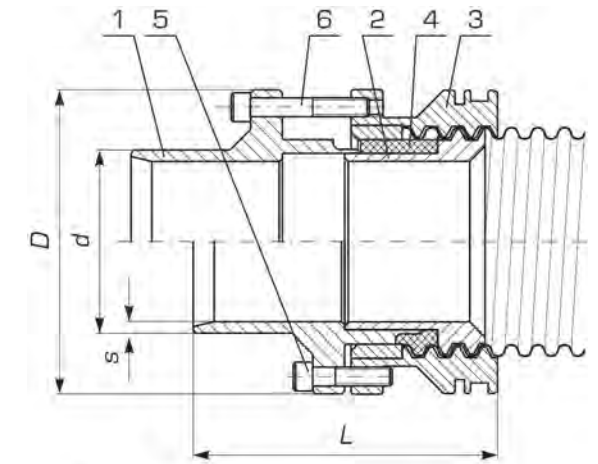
Фитинг обжимной под сварку ИЗОПРОФЛЕКС-135А
